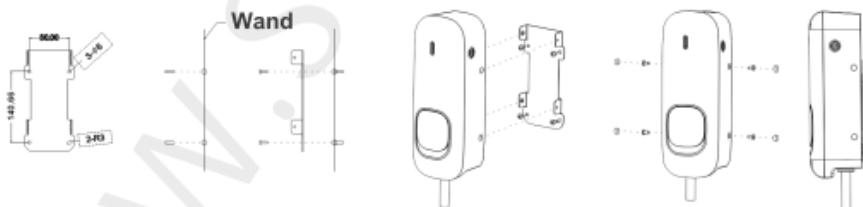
Installationsverfahren für die Wandmontage einer Ladestation Modus A
